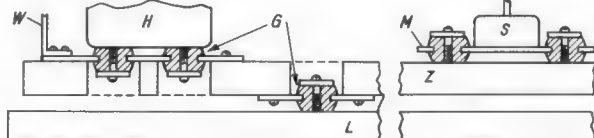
Befestigung der Einzelteile auf einer Zwischenleiste L und der Grundleiste L. W = Haltewinkel, H = Tonabnehmer (Hörersystem), G = Gummipuffer, M = Metallplatte, S = Schallfolien-schreiber
